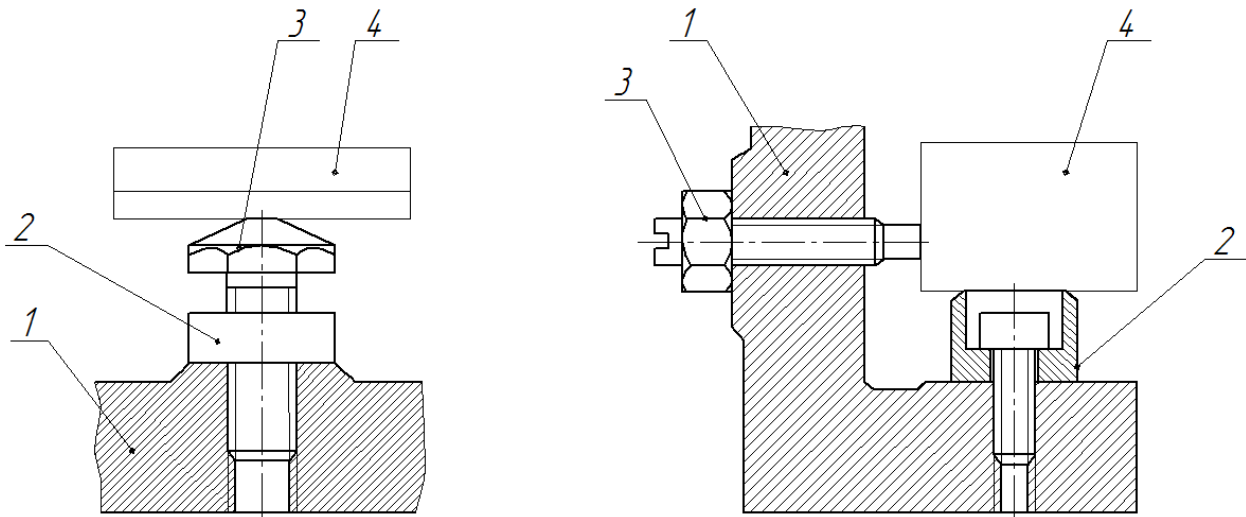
Будова регульованих гвинтових опор: 1 – корпус; 2 – опора; 3 – регулювальний гвинт; 4 – заготівка
